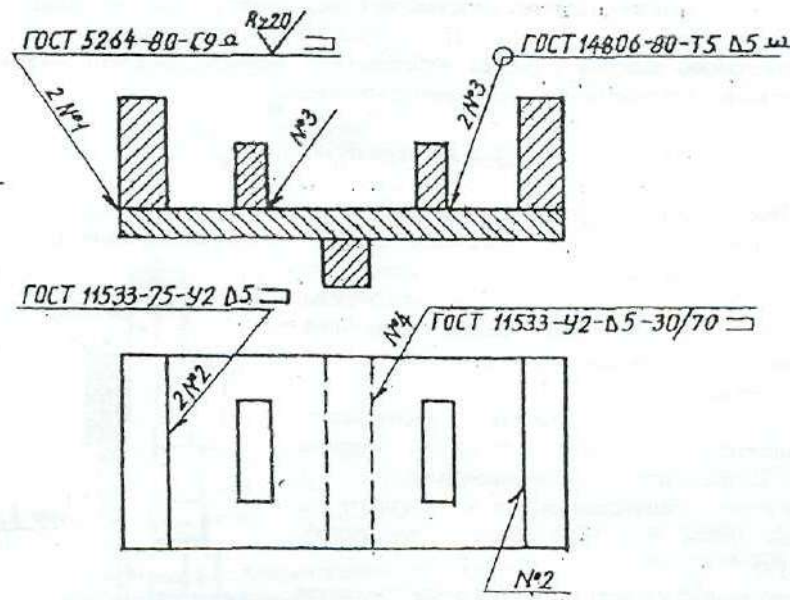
Условное обозначение сварных соединений
